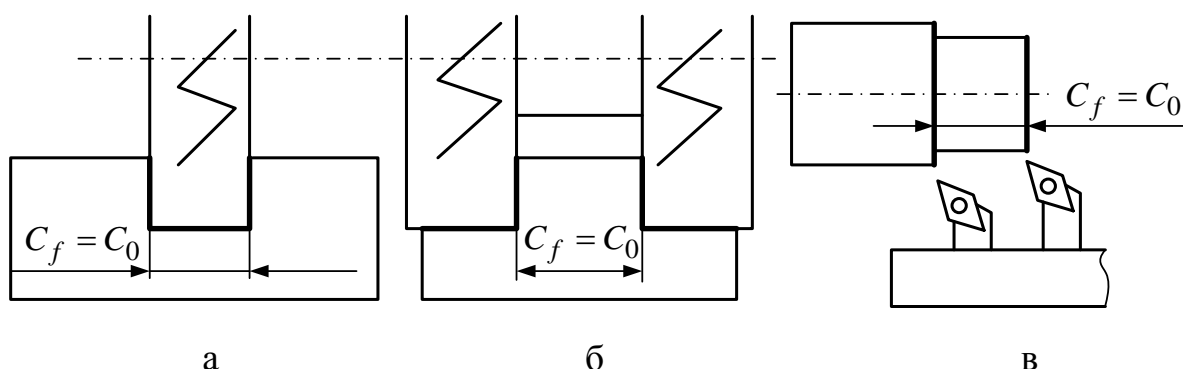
Схемы обработки поверхностей детали в размер за счёт точности собственно режущего инструмента (а) или за счёт точности установки двух режущих инструментов в инструментальной оснастке (б, в)
